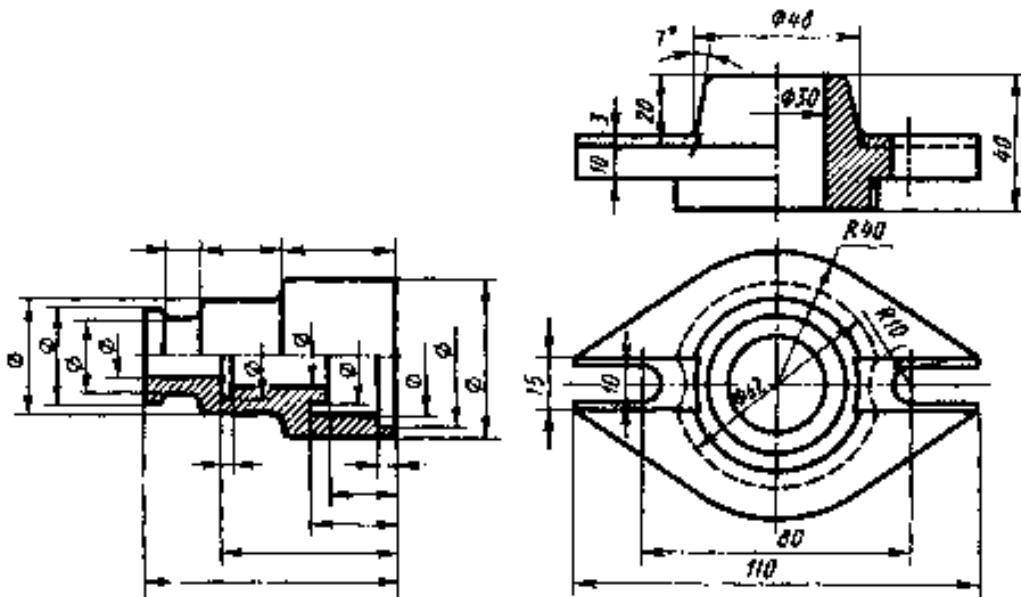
Пример простановки стрелок размеров на чертежах
